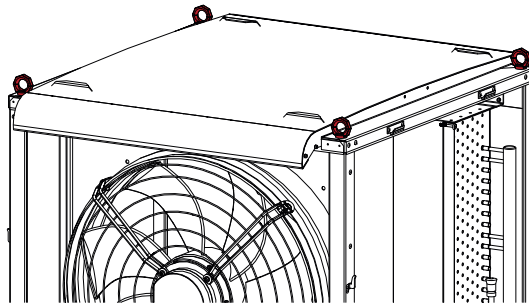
Wärmepumpe mit eingeschraubten Ringschrauben.
